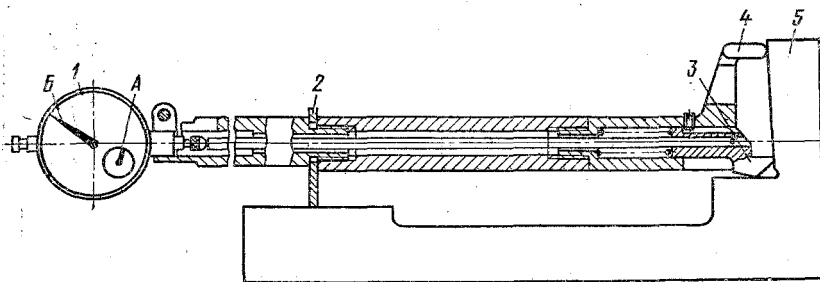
Схема настройки индикаторного прибора ИП-1Л по шаблону А6084-30708;
